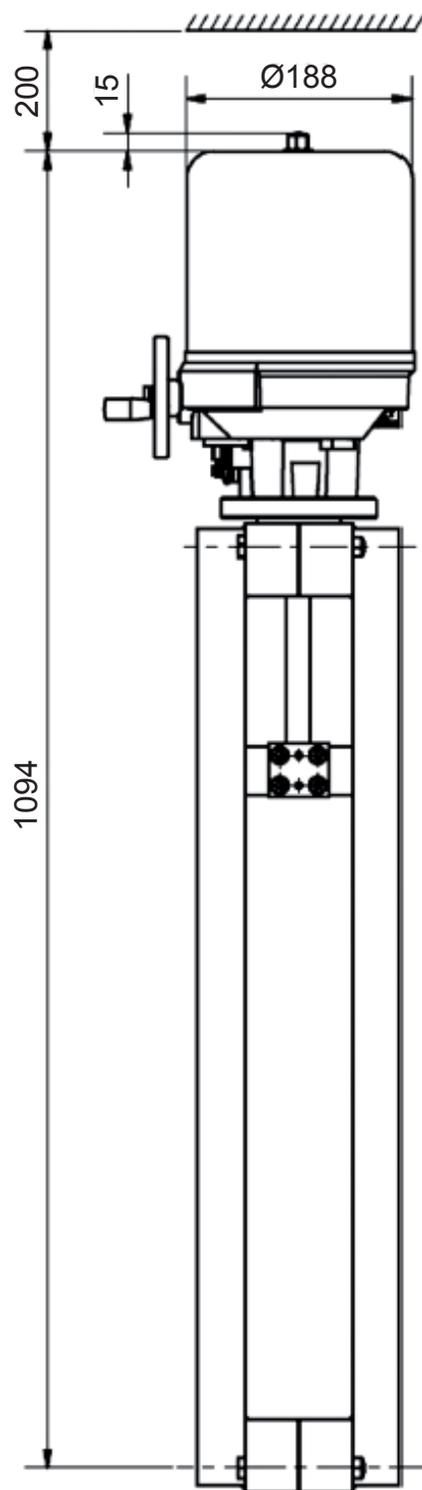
Maßzeichnung baelz E66 mit Ständer S41C
